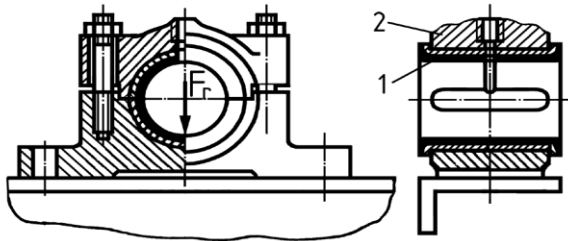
Конструкція підшипника ковзання у спеціальному корпусі
